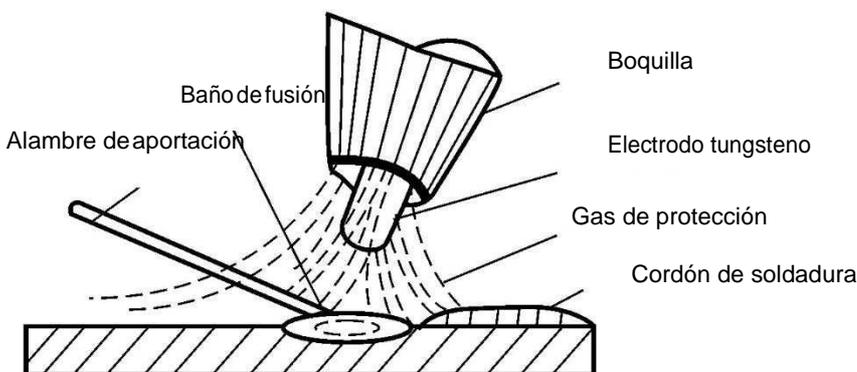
Croquis de la soldadura por arco con gas de protección Argón
